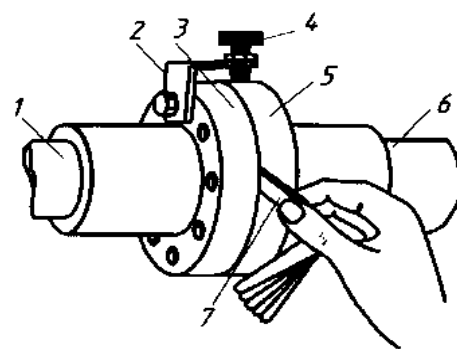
Центровка валов способом «обхода одной точкой»: 1, 6 — валы; 2 — скоба; 3, 5 — полумуфты; 4 — измерительный болт; 7 — щуп
